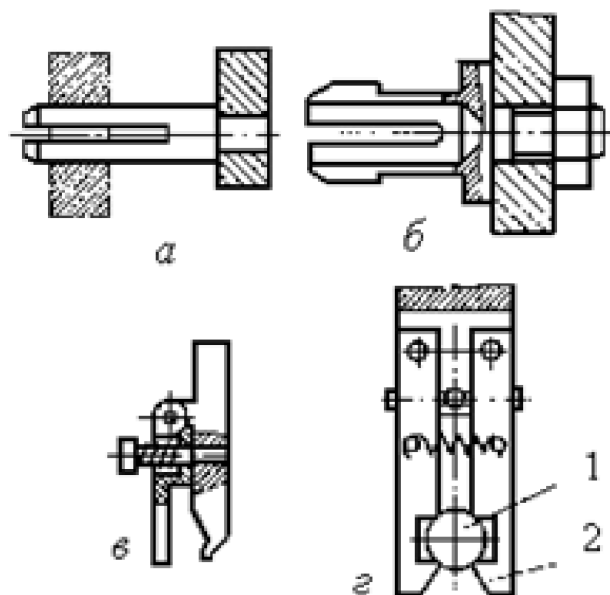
Некеровані захватні пристрої: а – типу пінцета у вигляді пружного розрізного валика, б – типу пінцета у вигляді розрізної пружної втулки, в – типу кліщів з однією рухомою губкою, г – типу кліщів з двома рухомими губками; 1 – заготовка; 2 – робочі елементи
